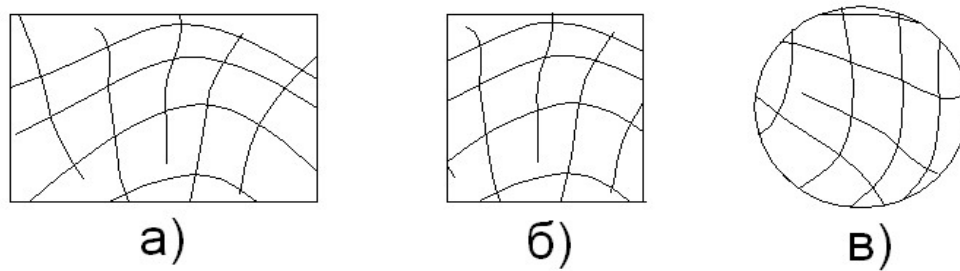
Для гнуття форми поперечного перетину заготовок
